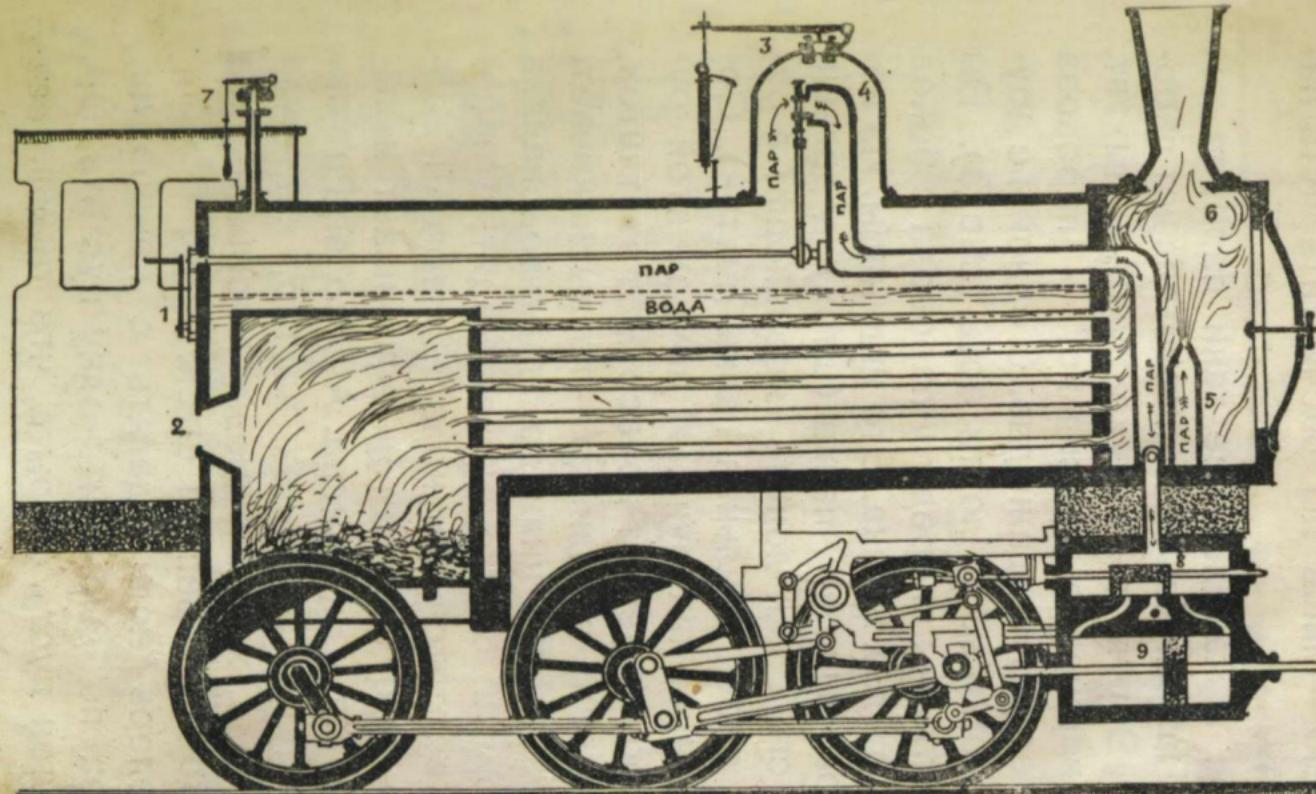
1—регулятор; 2—топка; 3—предохранительный клапан; 4—паровой колпак; 5—конус; 6—дымовая коробка; 7—свисток; 8—золотниковая коробка с золотником; 9—цилиндр.
